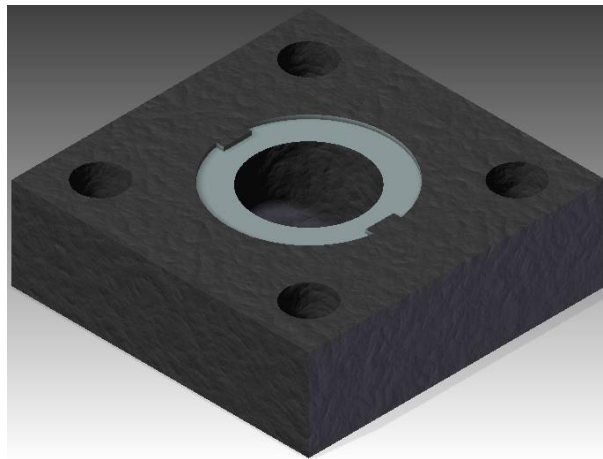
Molde para troquel para fabricación de una arandela hecho en solid edge
